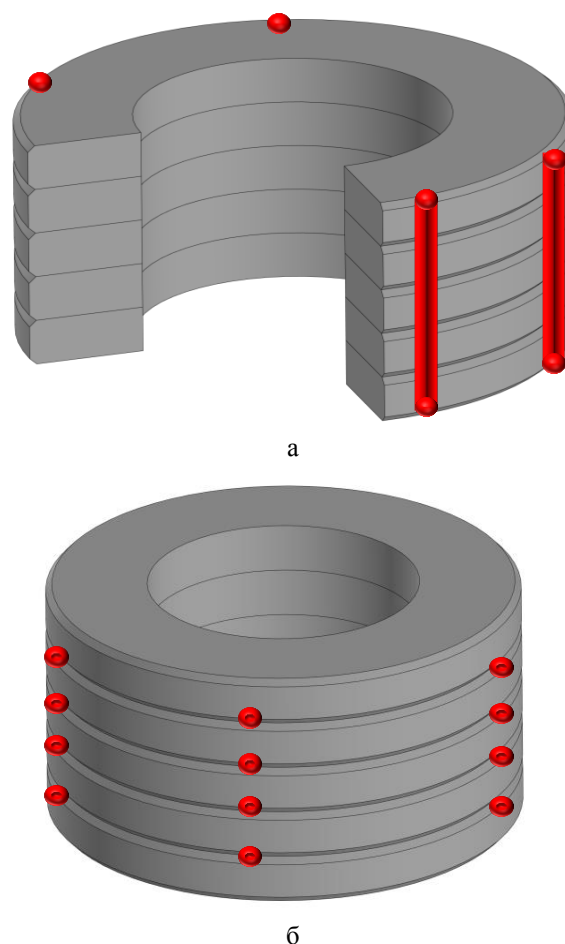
Изготовление переплавляемого электрода: а – путем нанесения сварных швов вдоль образующей цилиндра электрода; б – путем точечной сварки по внешней окружности контакта дисковых ножей
